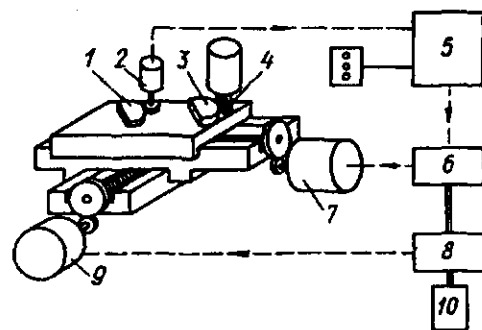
Схема двухкоординатного копирующе-фрезерного станка: 1 – копир; 2 – следящее устройство; 3 – заготовка; 4 – фреза; 5 – усилитель; 6 – генератор; 7 – двигатель следящей подачи; 8 – генератор; 9 – двигатель следящей подачи; 10 – электродвигатель
